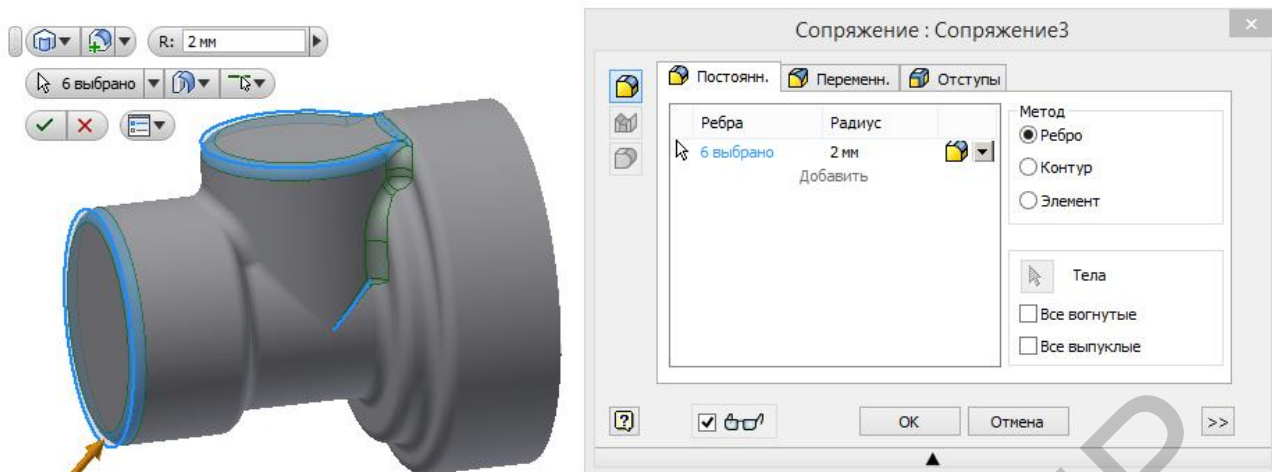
Одна из стадий нанесения литейных сопряжений на кромки заготовки корпуса
